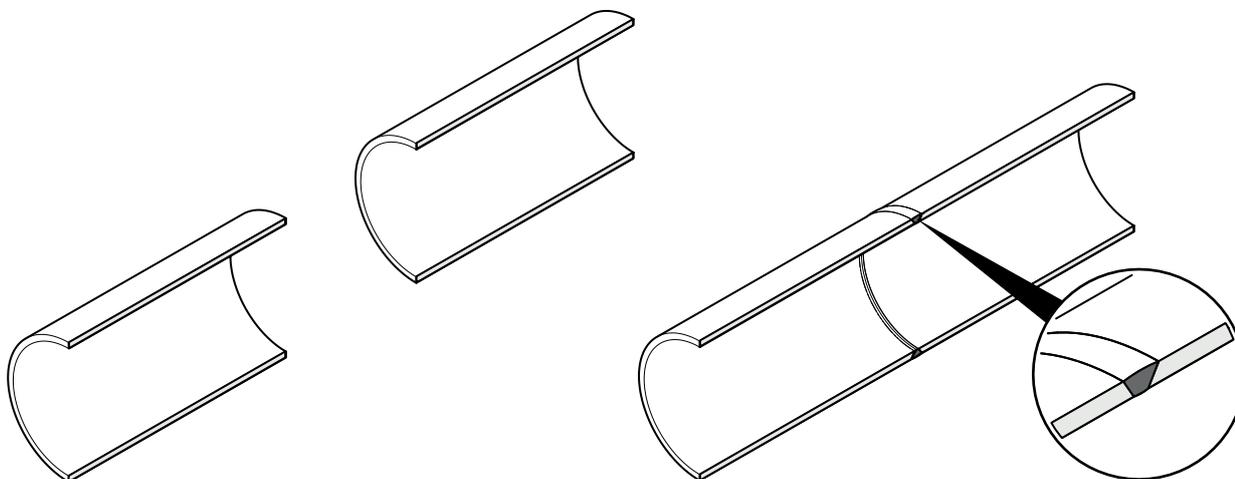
Assemblage par soudure (ouvert/soudé)
